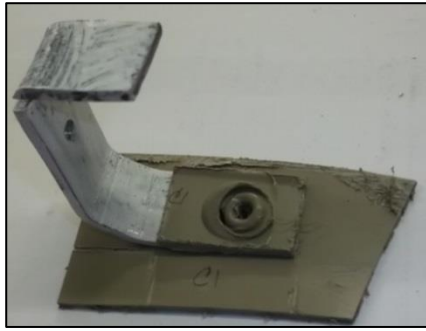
Geometría y dimensiones de primer corte de probetas.
